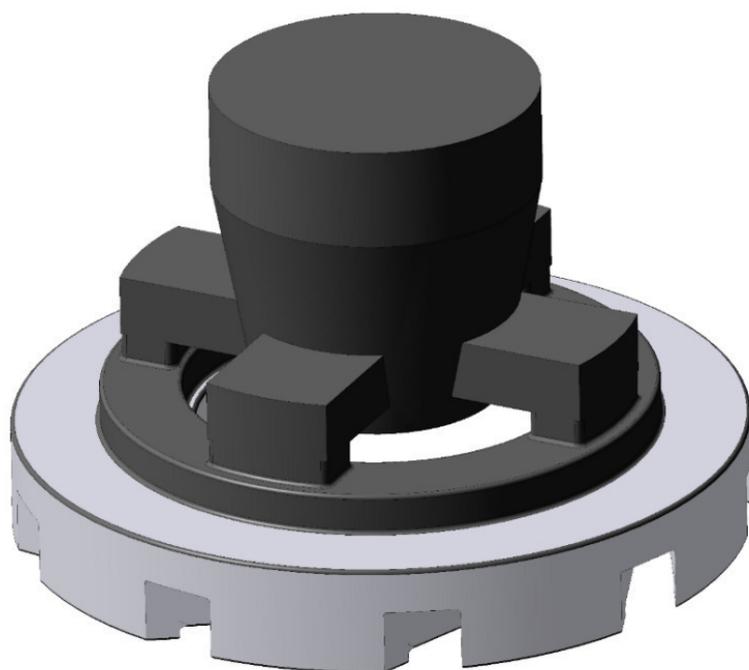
Трехмерная модель отливки с прибылью и литниковой системой
